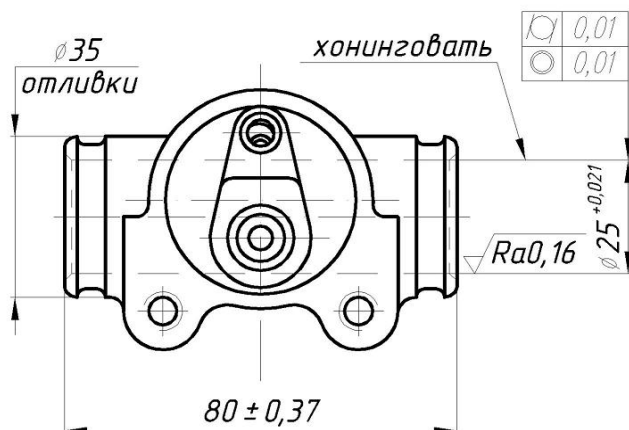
Технологический чертеж колесного цилиндра заднего тормоза 3151-3502046 автомобиля УАЗ
